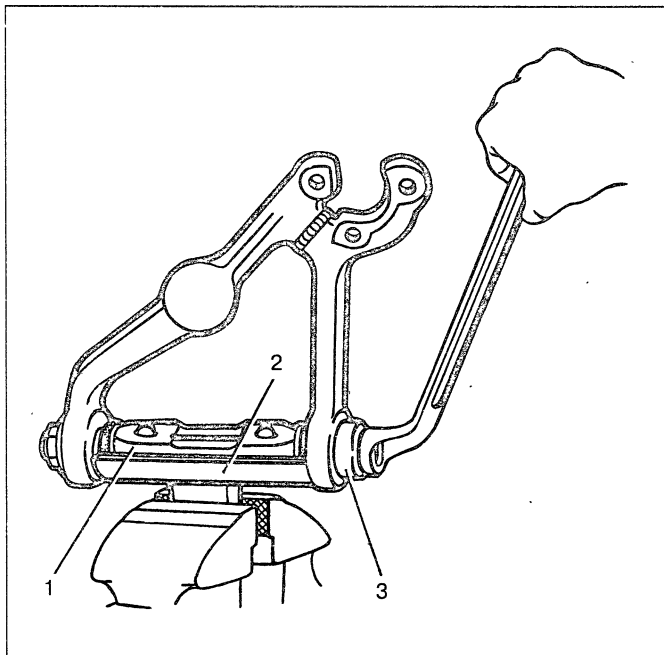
Запрессовка шарниров верхнего рычага: 1 – ось рычага; 2 – приспособление 67.7853.9519; 3 – приспособление А.74177/1
